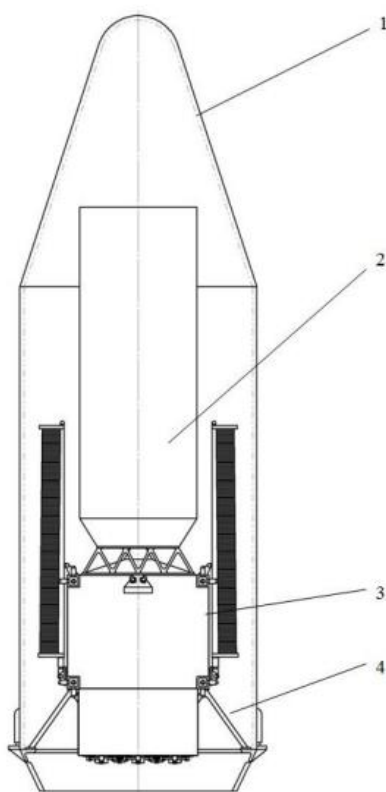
Компоновка КА под обтекателем РН:
